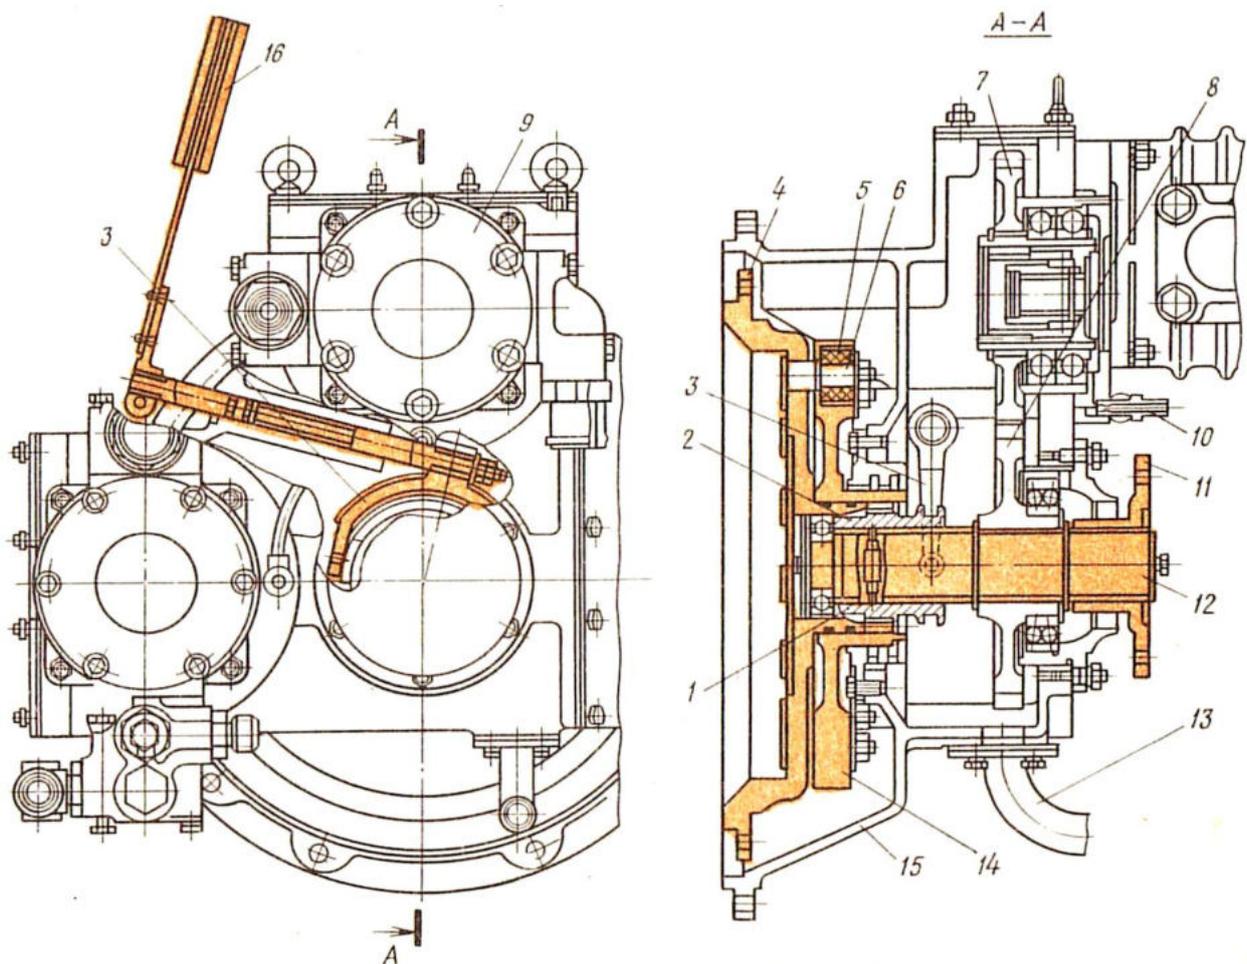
Полужесткая муфта и редуктор привода насосов трактора К-701:
